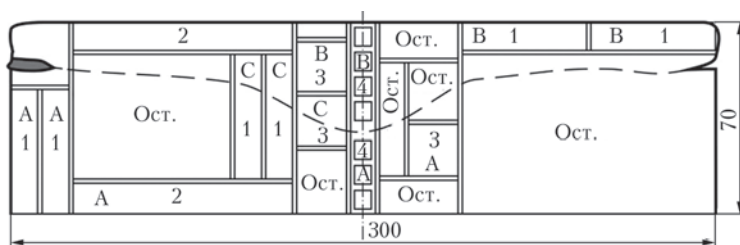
Схема вырезки образцов: зона А — основной металл; В — наплавленный металл; С — переходной слой
